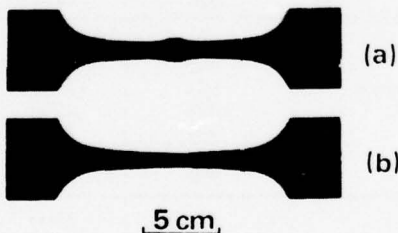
Eprouvettes soudées avant essai.
